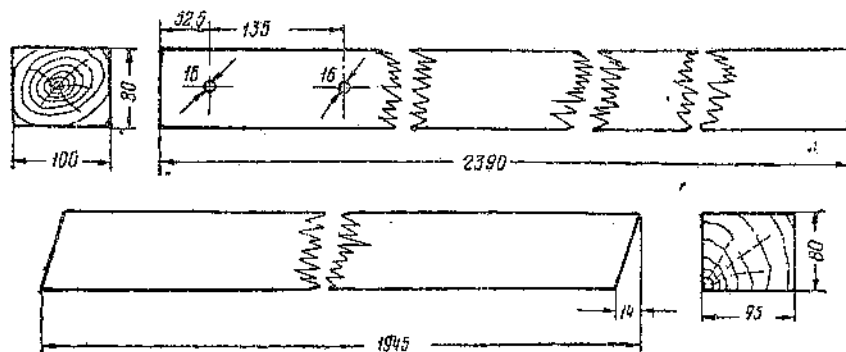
Изготовление верхних брусков люкового отверстия из старых лобовых фрамуг
